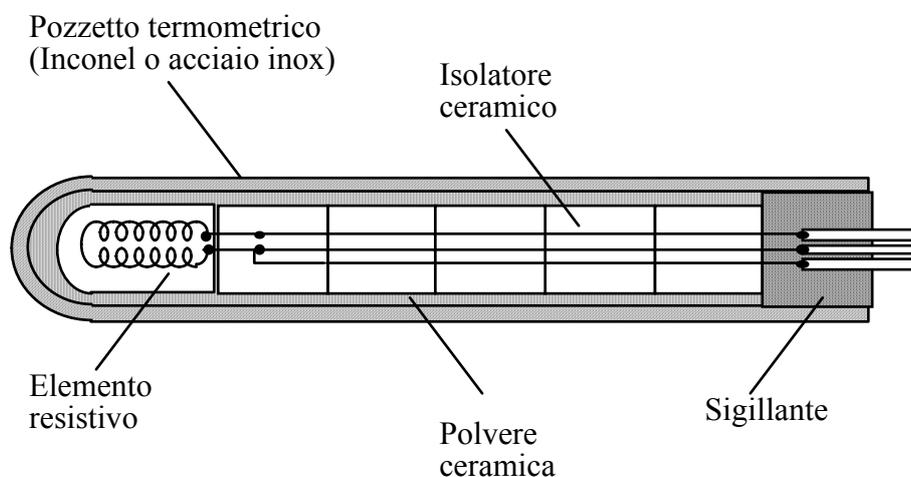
Assemblaggio di un termometro a resistenza industriale ad immersione
